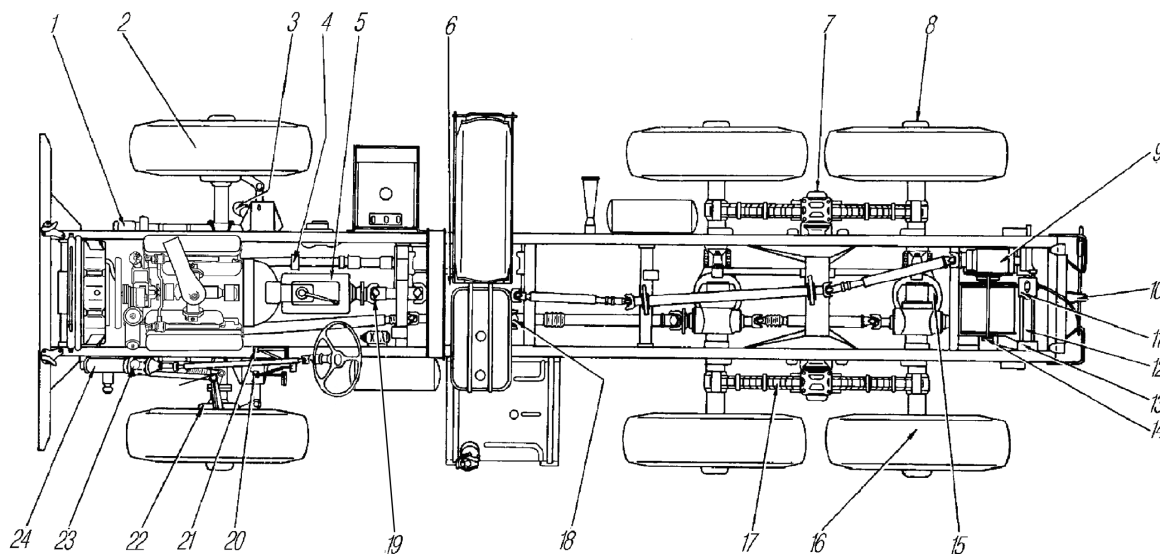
Схема смазки автомобиля 6x6
